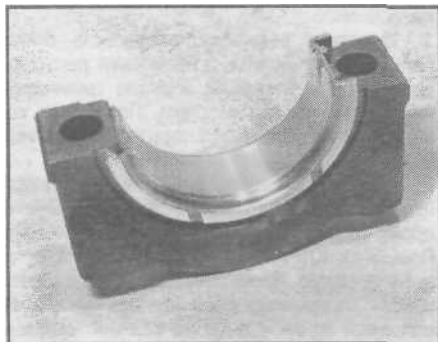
,г. Установка вкладыша с фланцами в крышку среднего подшипника
